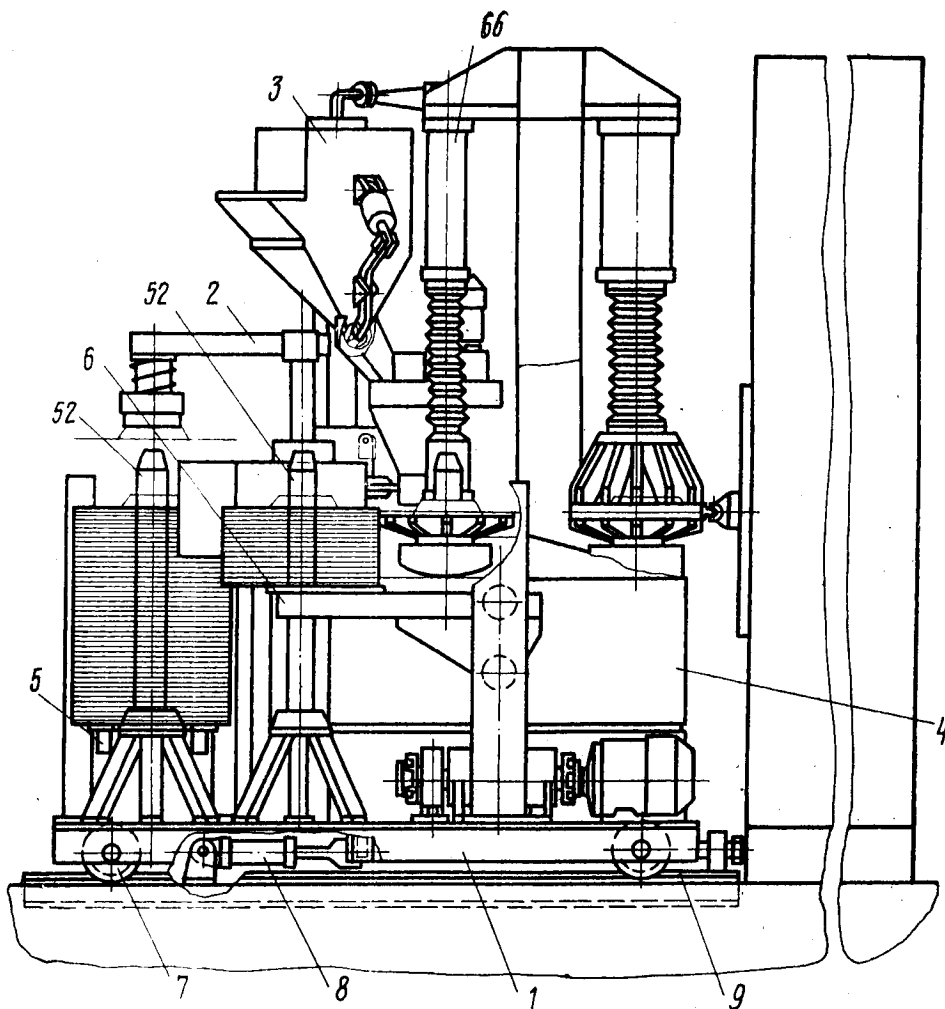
Механізована лінія для неперервно-послідовного індукційного наплавлення дисків, загальний вигляд
